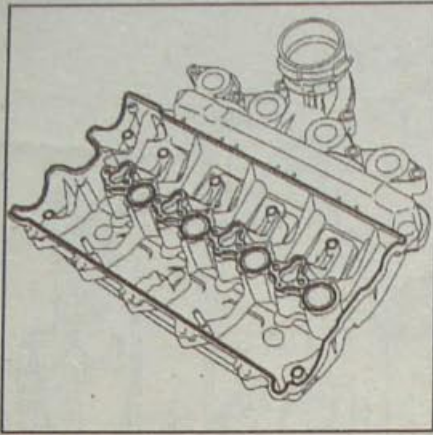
Расположение прокладки впускного коллектора–крышки головки блока цилиндров
